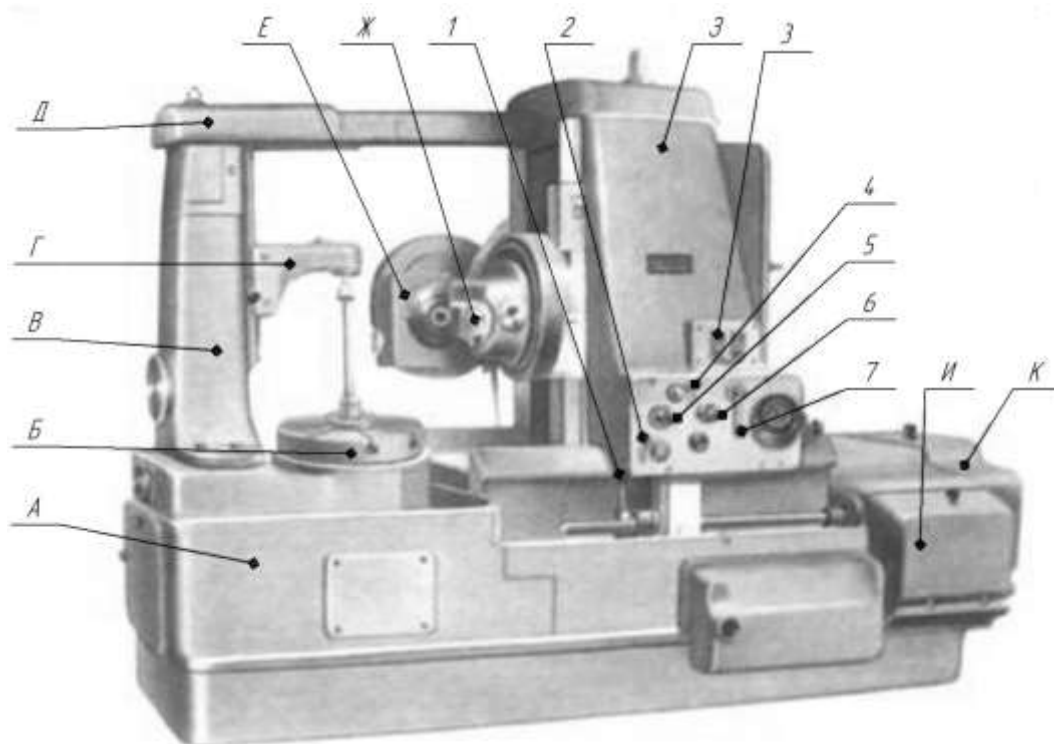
Общий вид зубофрезерного полуавтомата модели 5Д32
